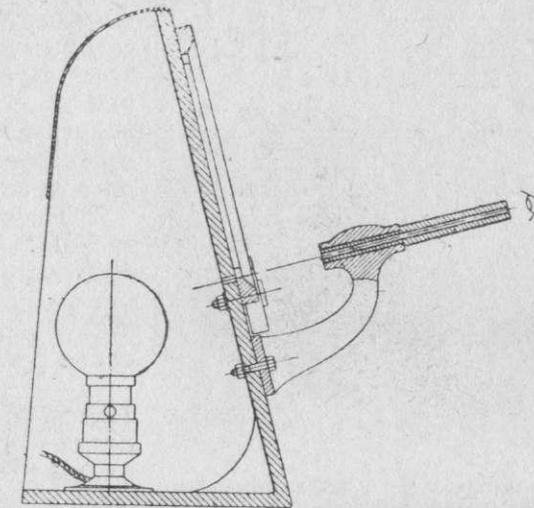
Приспособление для проверки поршневых колец на прилегание к стенкам цилиндра.
